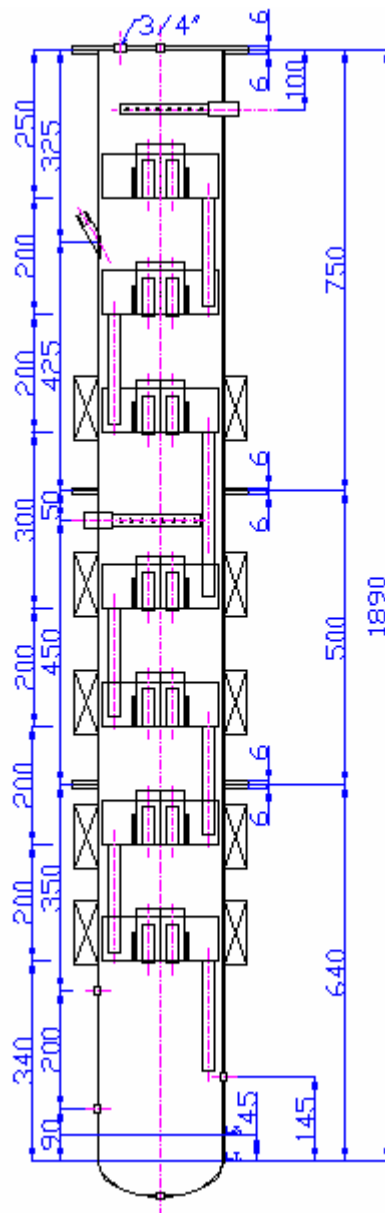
7- Plano constructivo de la columna de destilación C-02.
